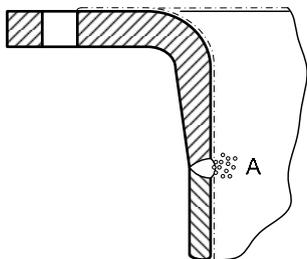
Нарушение эмалевого покрытия в месте сварного шва
